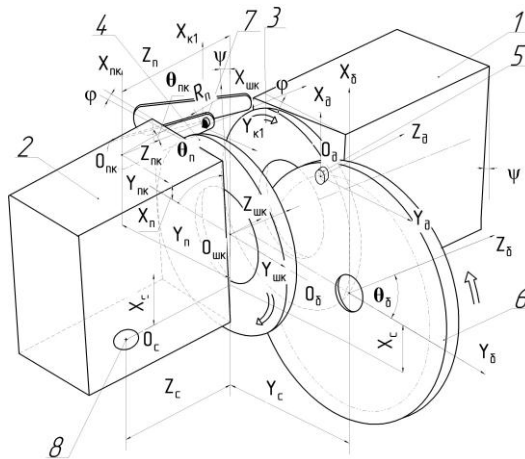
Розрахункова схема формоутворення торців хрестовин карданних валів
